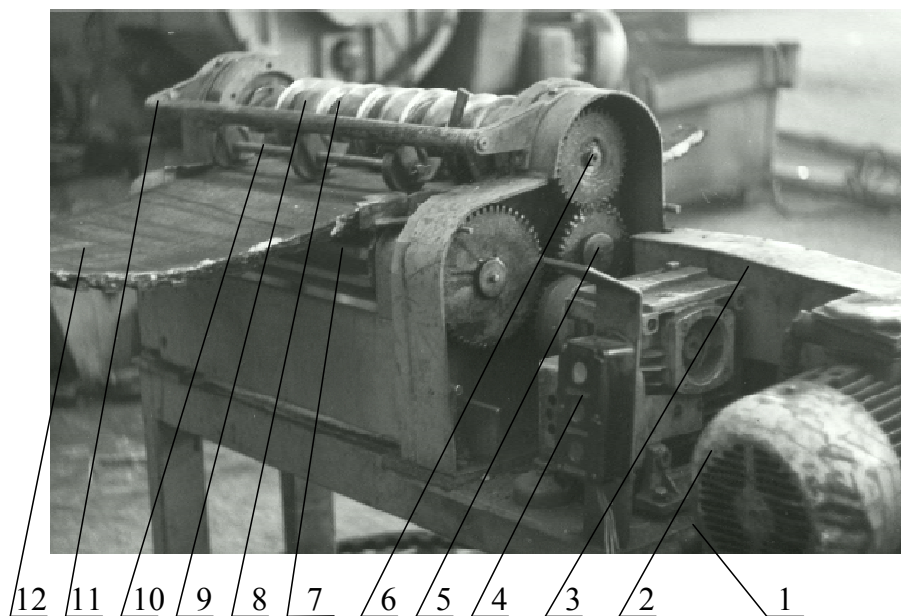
Загальний вигляд установки для розрізання конвеєрної стрічки з п'ятьма ножовими блоками
